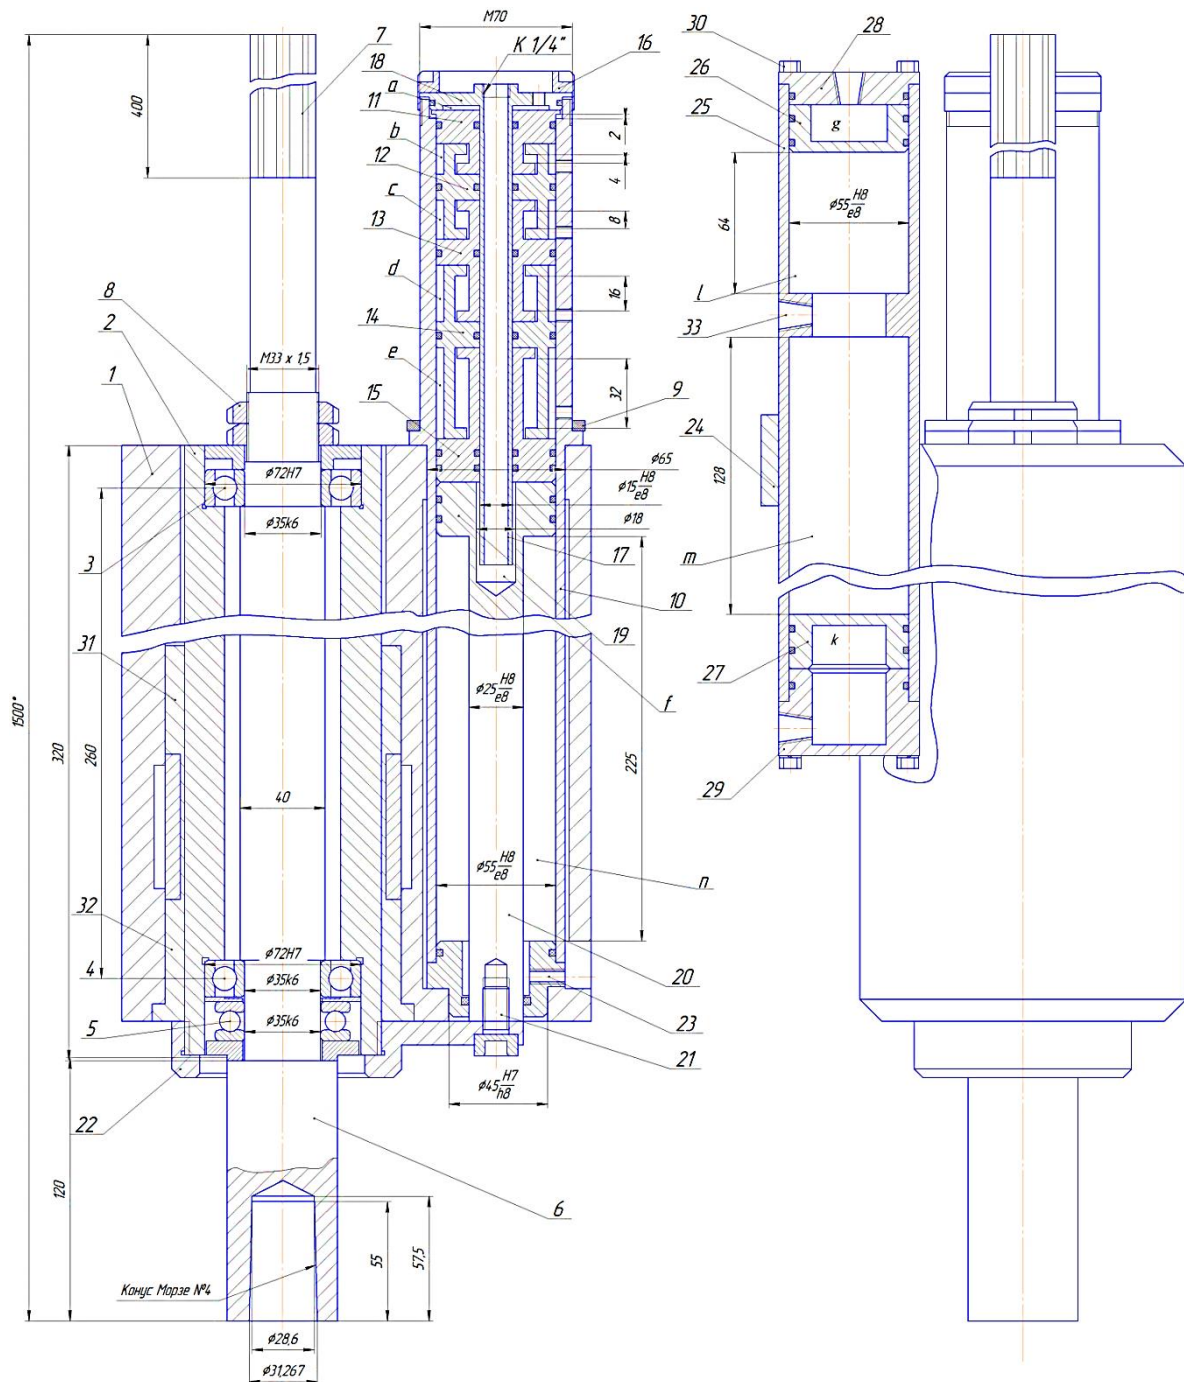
5 Привод подачі шпинделя свердлильного верстата.[11]
